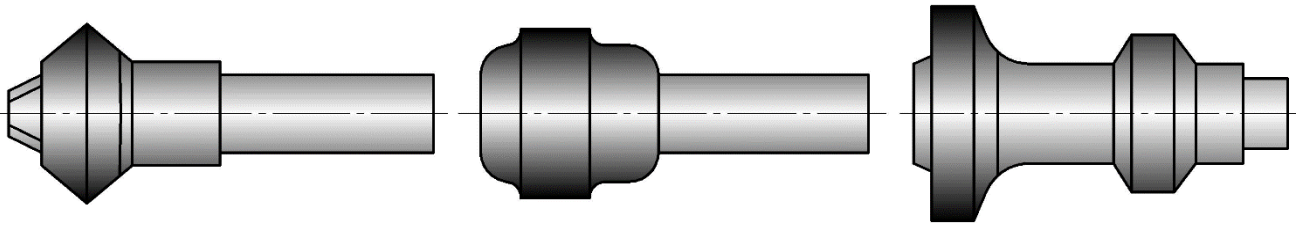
Заготовки для зубчастих коліс, отримані на ГKM
